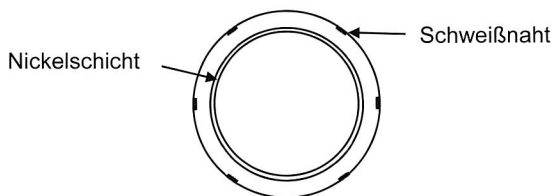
Ringkernmuster mit Schweißnähten und Nickelbeschichtung
